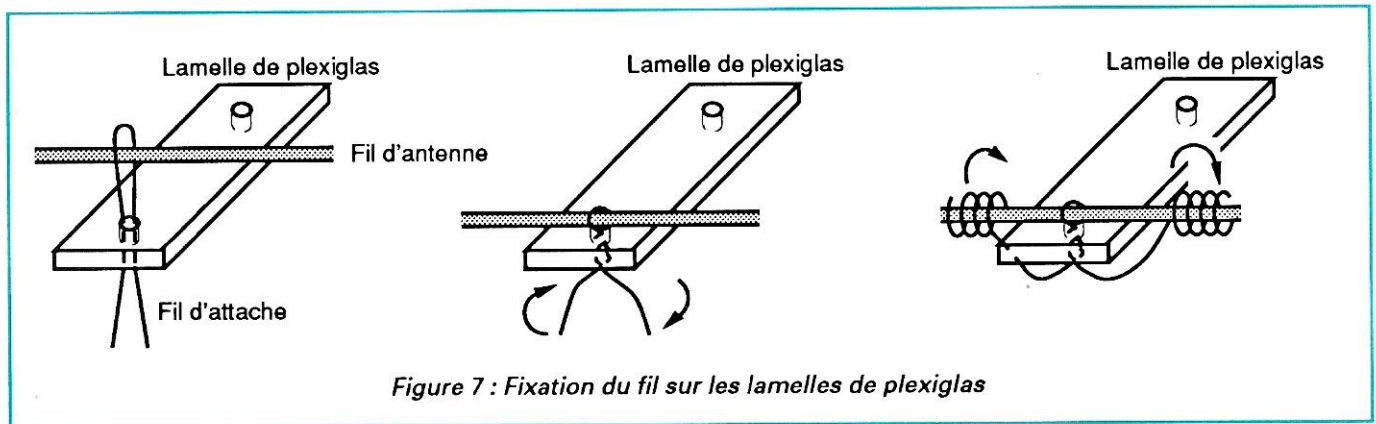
Fixation du fil sur les lamelles de plexiglas
